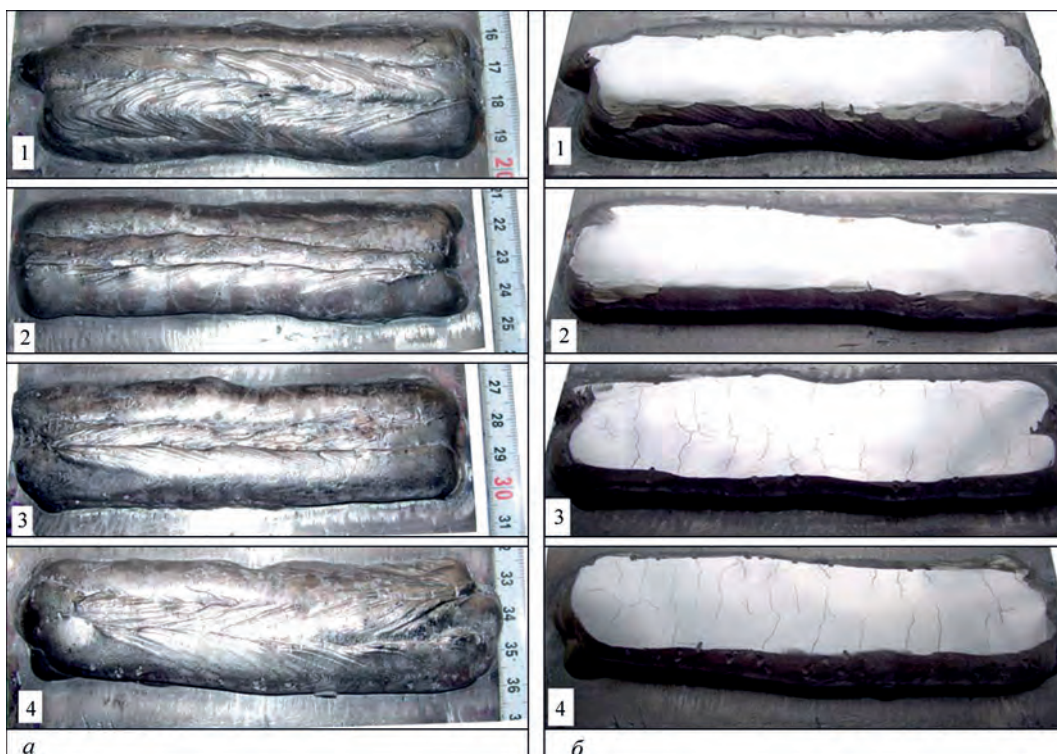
Зовнішній вигляд зразків зі сталі 40Х після наплавлення (а) і механічної обробки (б). Вміст бору в наплавленому металі, %: 1 – 0; 2 – 0,007; 3 – 0,02; 4 – 0,04
